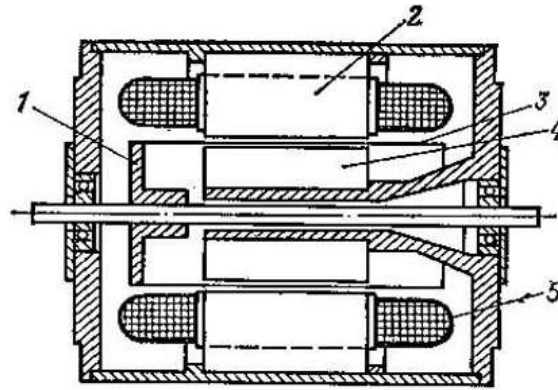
Máquina asincrónica bifásica con rotor hueco
